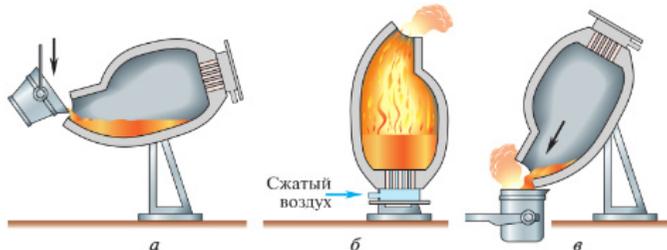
Процесс выплавки стали в конверторной печи: *а* — заливка чугуна; *б* — продувка (выжигание углерода); *в* — выпуск стали
